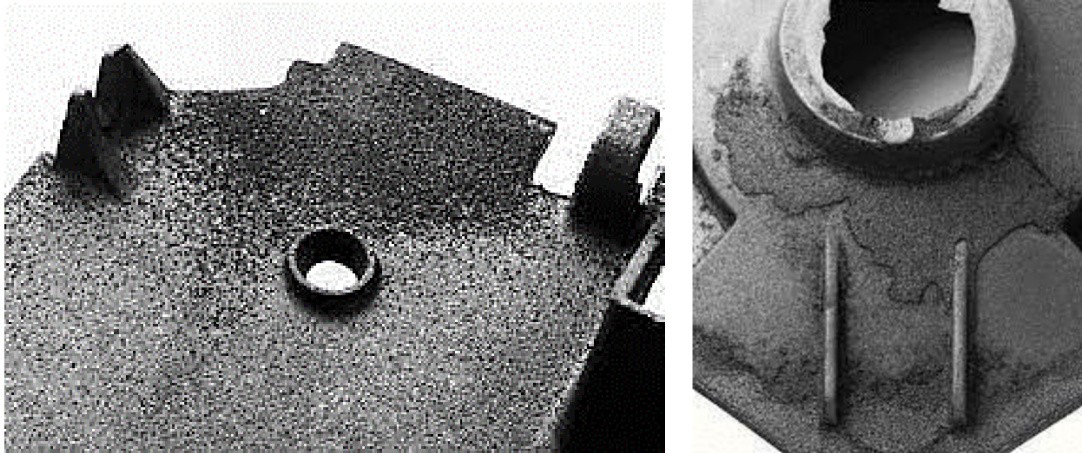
Příklad vady „drsný povrch“ (místa hlubší penetrace [11]).
